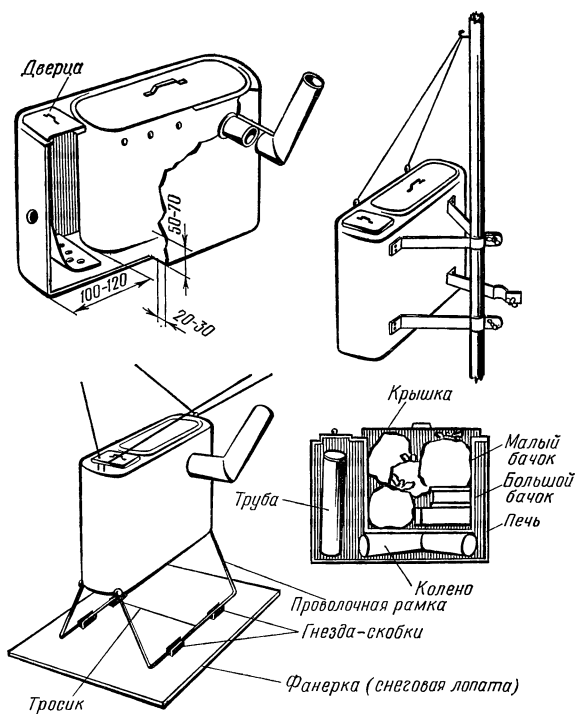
Печь для варки пищи, установка ее и транспортное положение.
